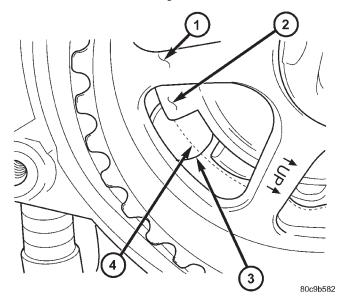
CARA DEL SENSOR DE CMP EN LA RUEDA DE DIRECCION - 2.4L
